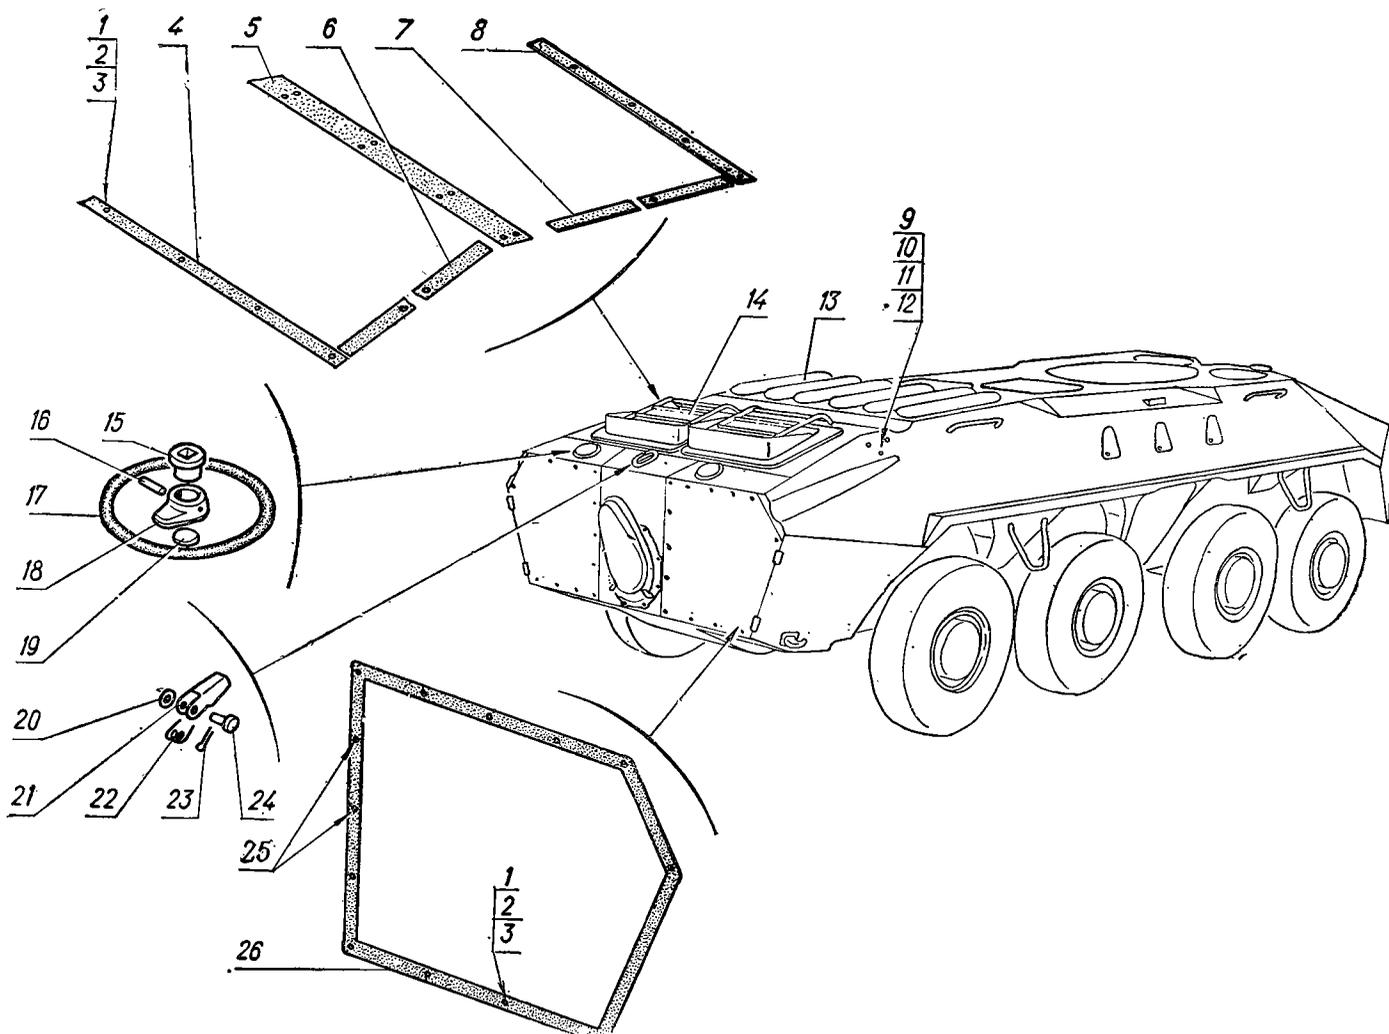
Корпус, буксирные крюки, люки корпуса, днище, замок крышки люка № 7
